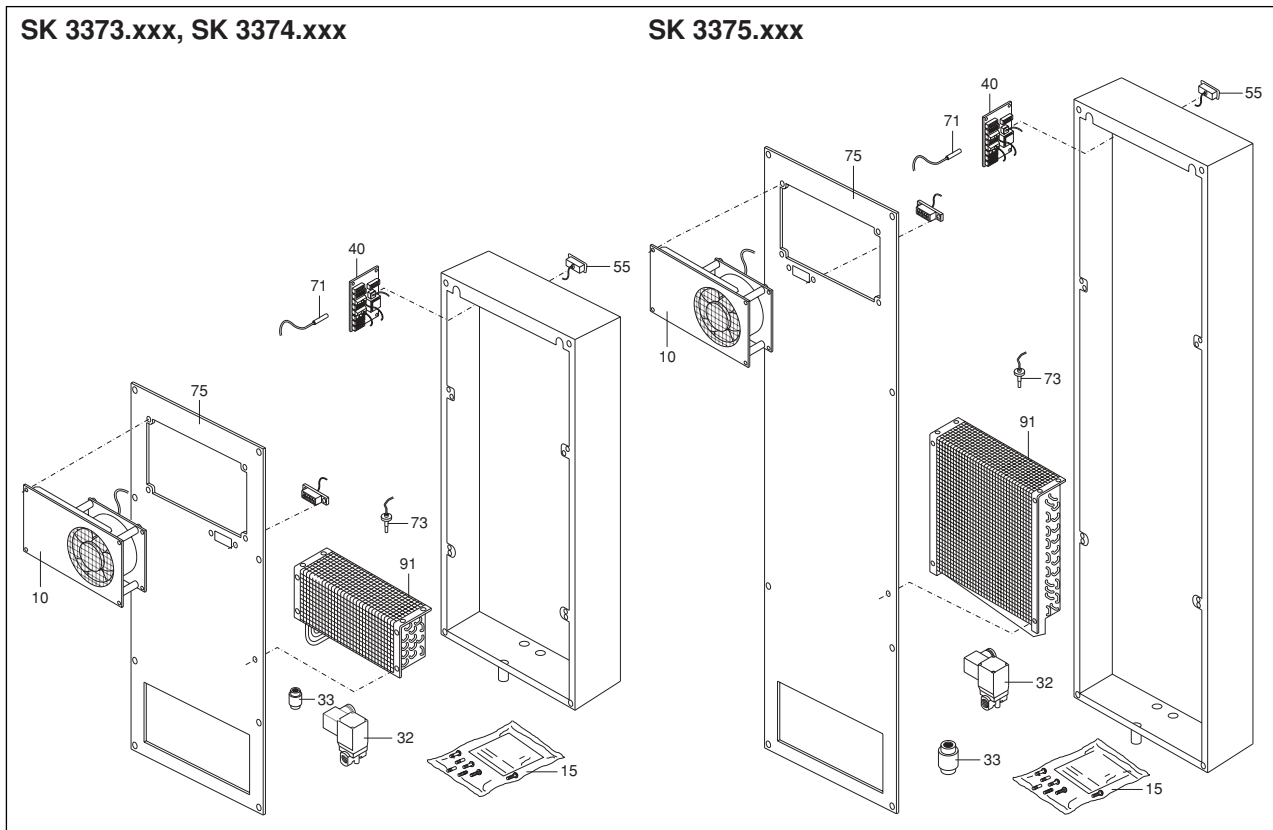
Parti di ricambio per SK 3373.xxx/SK 3374.xxx e SK 3375.xxx
